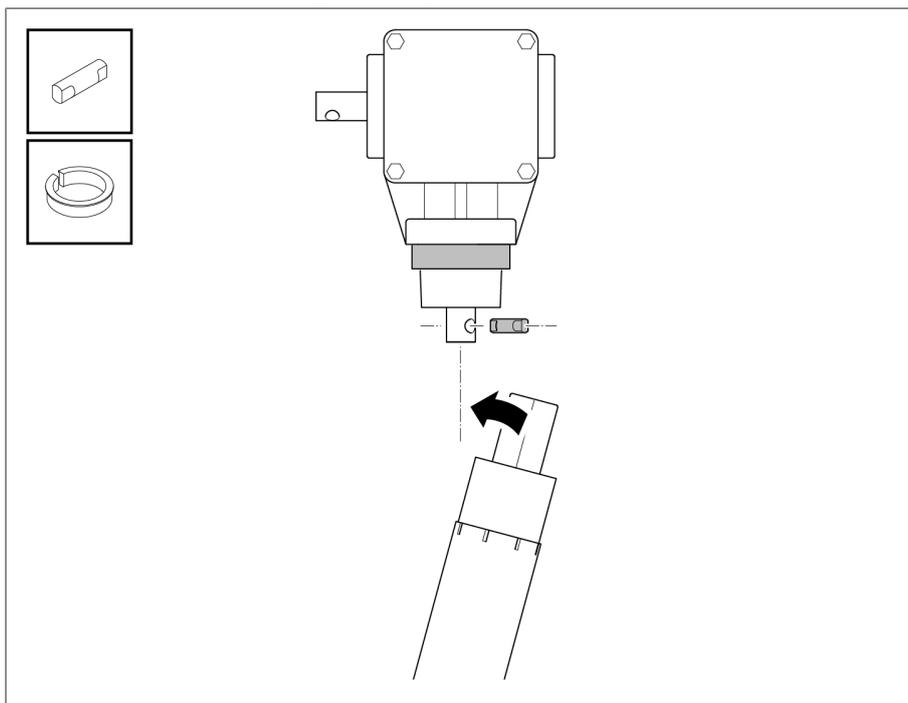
Colocar o anel adaptador e o pino de acoplamento
